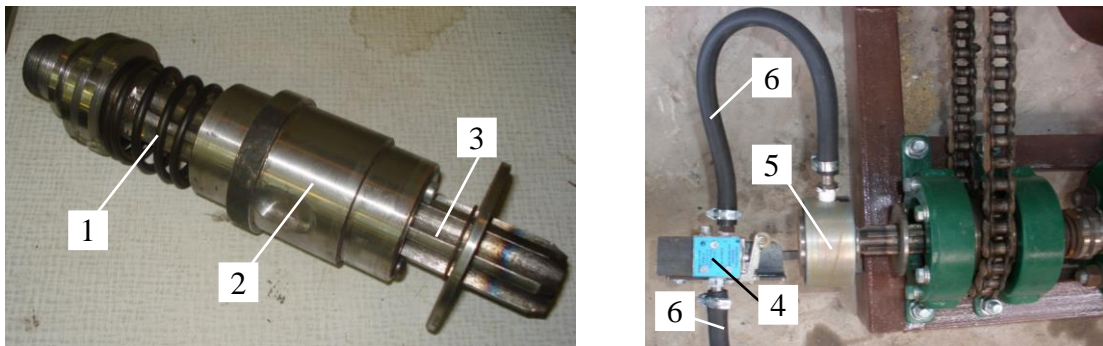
Механізм увімкнення пневморозподільника: 1 – пружина стиснення; 2 – корпус; 3 – шліцьовий вал з напівкруглими канавками; 4 – пневморозподільник; 5 – обертовий пневмоперехід
